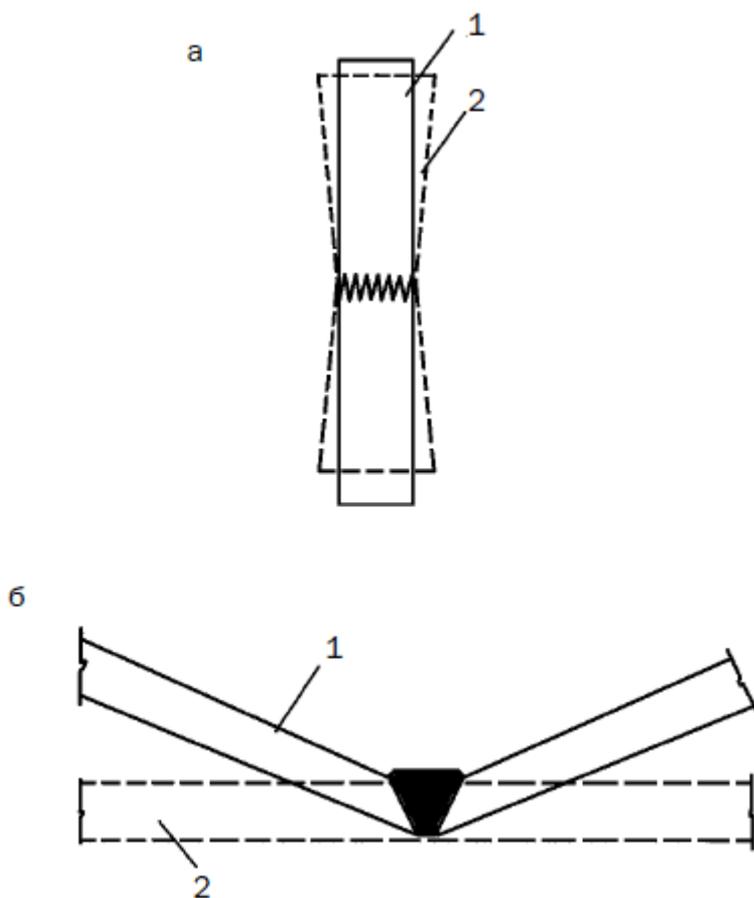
Некоторые виды деформации: а – в плоскости сварного соединения; б – вне плоскости сварного соединения; 1 – форма изделия до сварки; 2 – форма изделия после сварки
